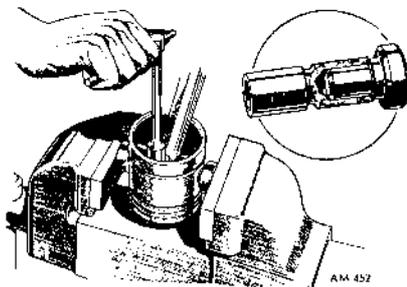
Zum Lösen und Festziehen der Kolbenbolzen-Sicherungsschraube klemmt man den Kolben am besten auf diese Art in den Schraubstock. Die dazu nötigen speziellen Haltebolzen, die man beidseitig in die Kolbenbolzenbohrung einführt, lassen sich leicht selber herstellen (siehe Kreis).
